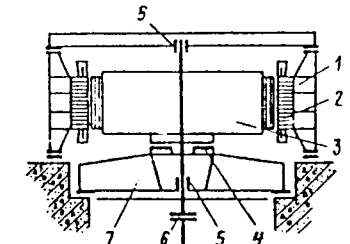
Гидрогенератор зонтичного исполнения с опорой на нижнюю крестовину: 1 — корпус; 2 — статор; 3 — ротор; 4 — подпятник; 5, 8 — направляющие подпятники; 6 — муфта; 7 — нижняя крестовина
